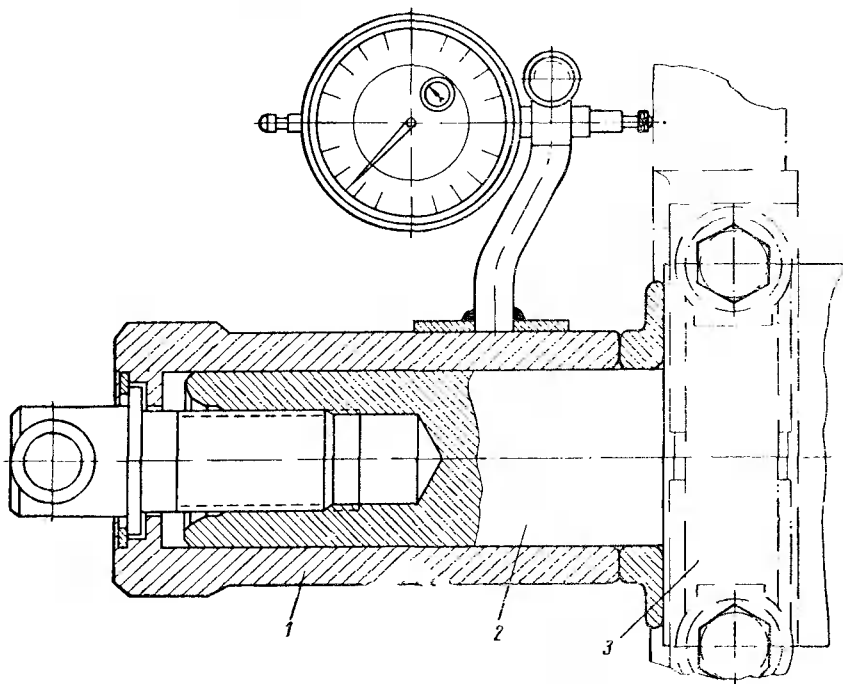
Схема проверки осевого люфта коленчатого вала у двигателя ЗИЛ-130:
